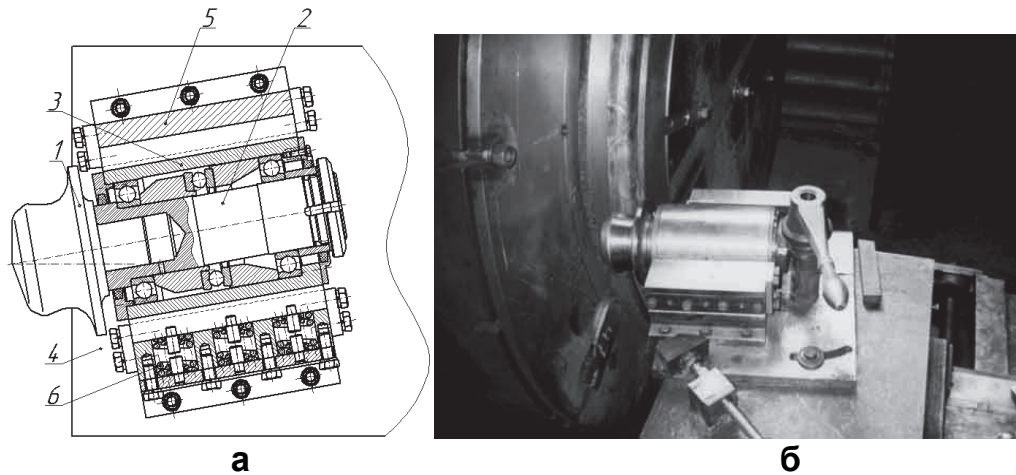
Конструкція розкочувальної головки (а) і загальний вигляд розкочувальної приставки до лобового токарного верстата (б):
